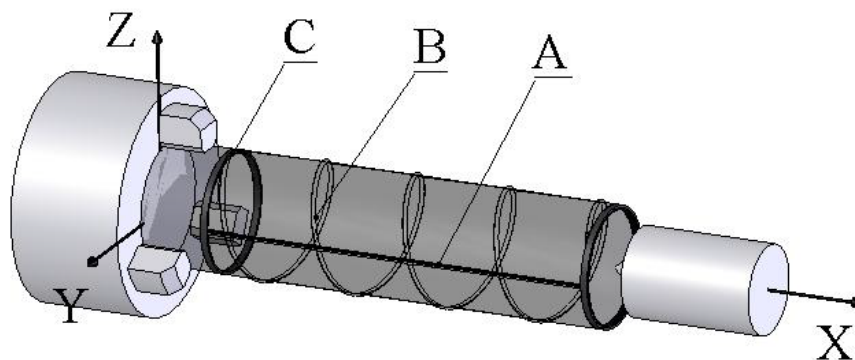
Можливі траєкторії руху вимірювального інструмента навколо деталі циліндричної форми
